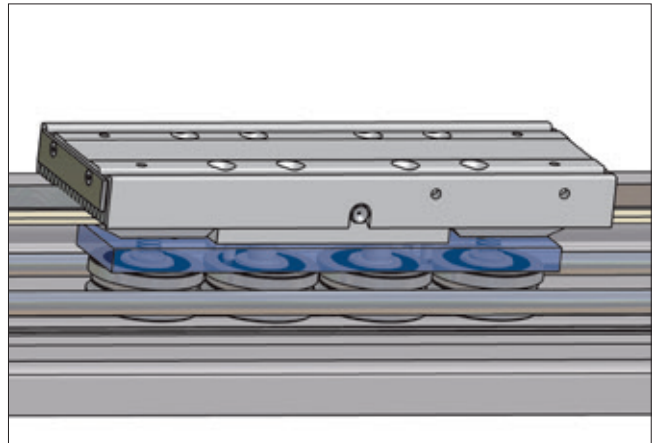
NTN-SNR – Linearachse mit Laufrollenführung
